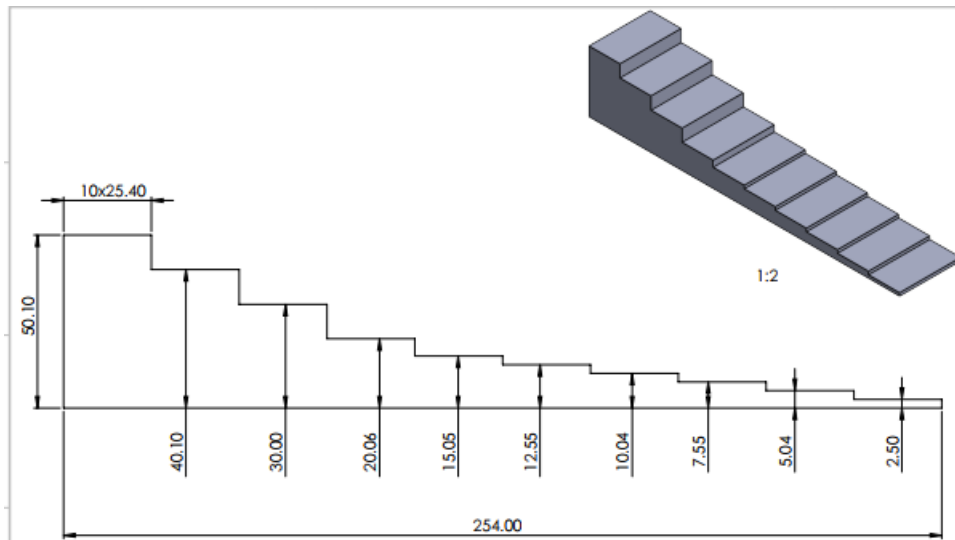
Vista in sezione ed assometrica della 'scaletta'
